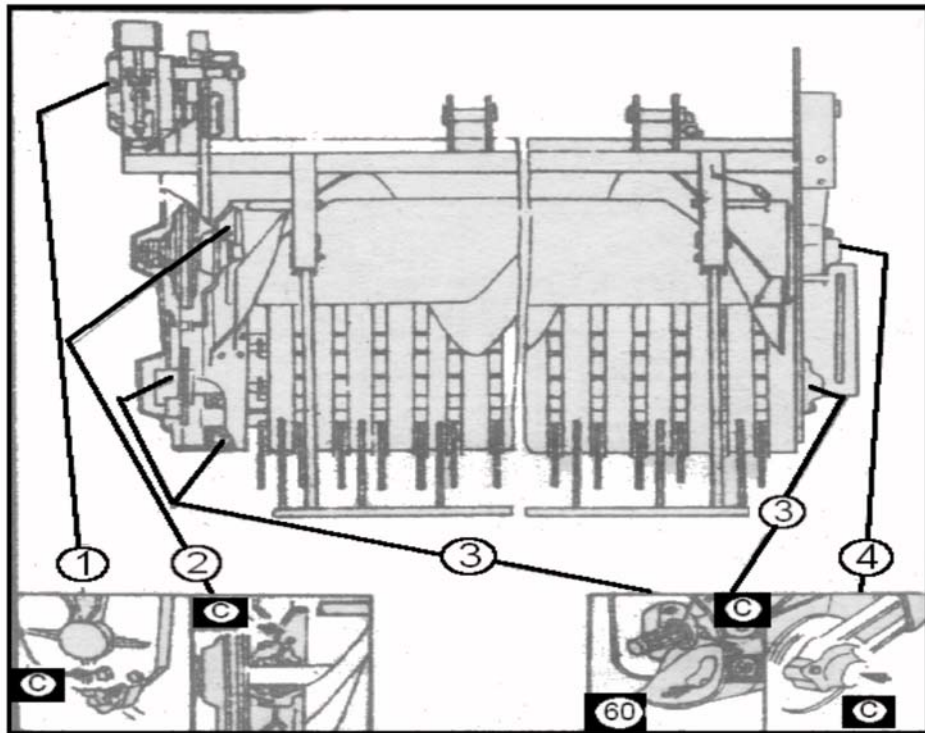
Схема смазки подборщика с качающимися рычагами
